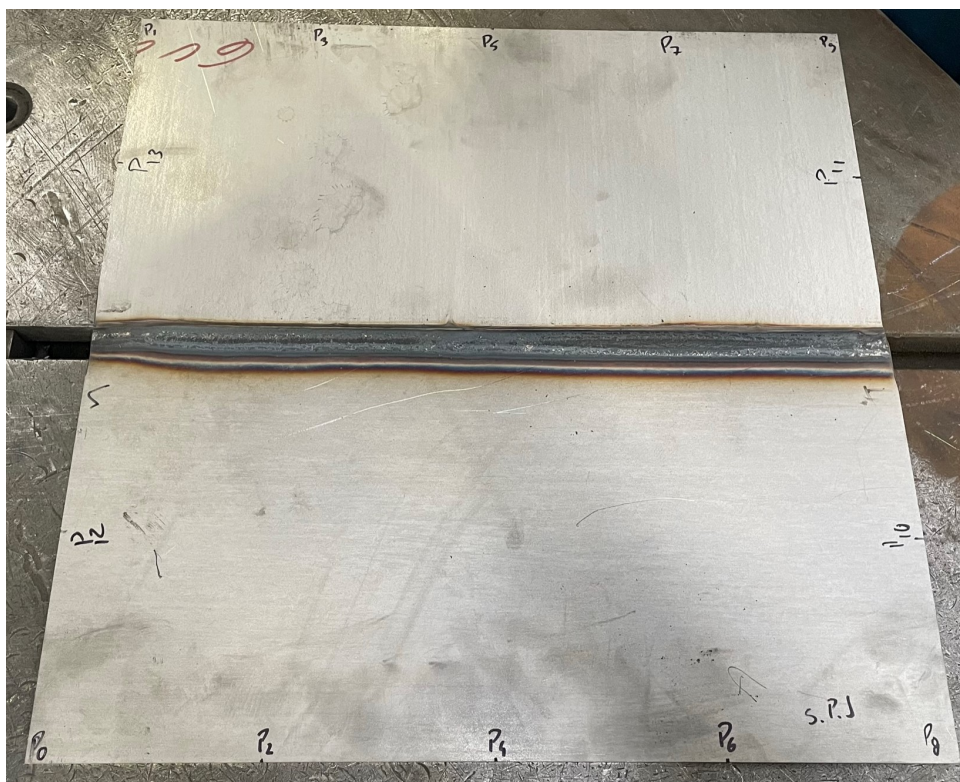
Provete após soldadura com máquina TIG convencional.
